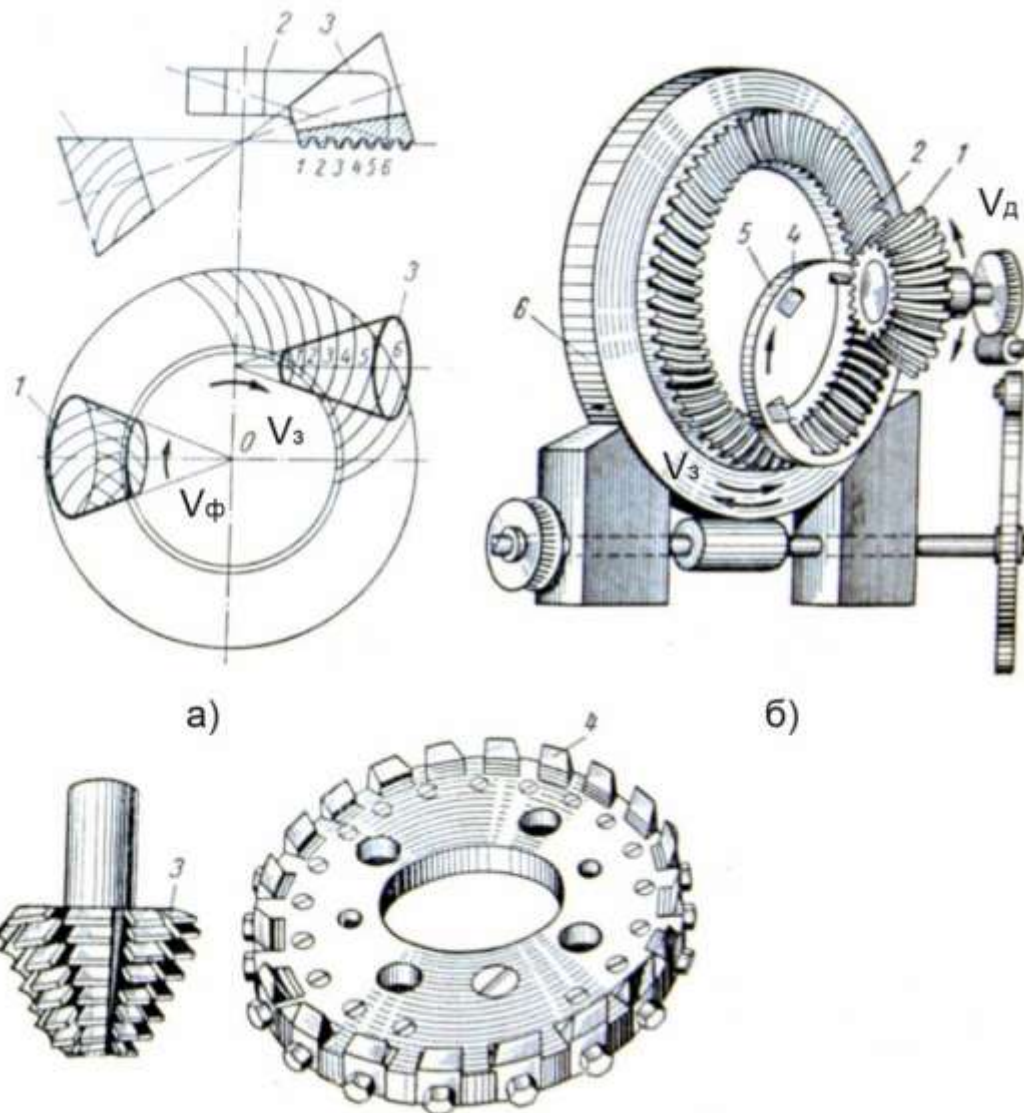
Схема нарізування зубів конічних зубчастих коліс із криволінійними зубами: а – черв'ячною конічною фрезою; б - різцевою головкою.
